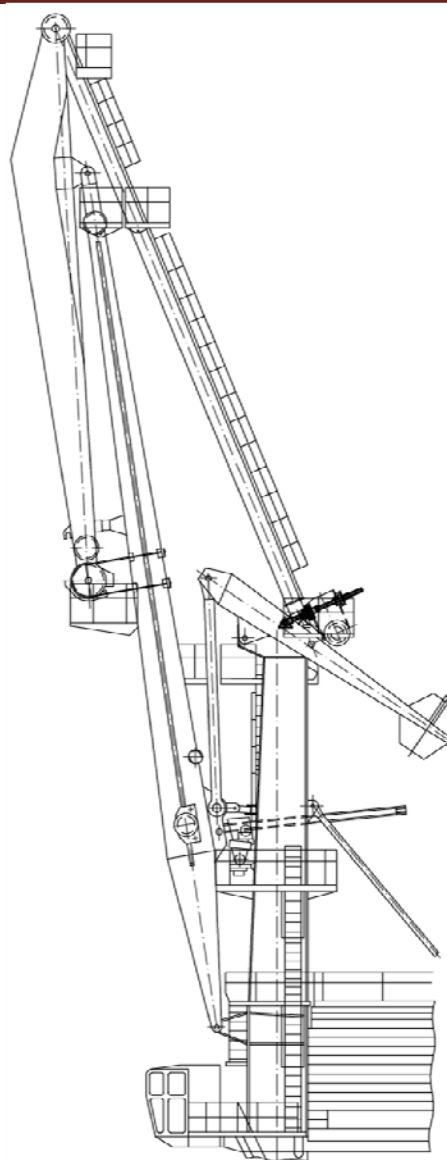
Схема разгрузки шарнира «Колонна – жесткая оттяжка» с выводом жесткой оттяжки.
